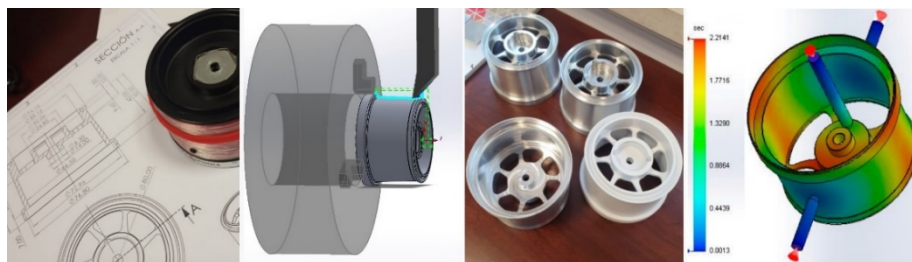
Del diseño a la fabricación del elemento "bobina": torneado-fresado vs. moldeo por inyección.
